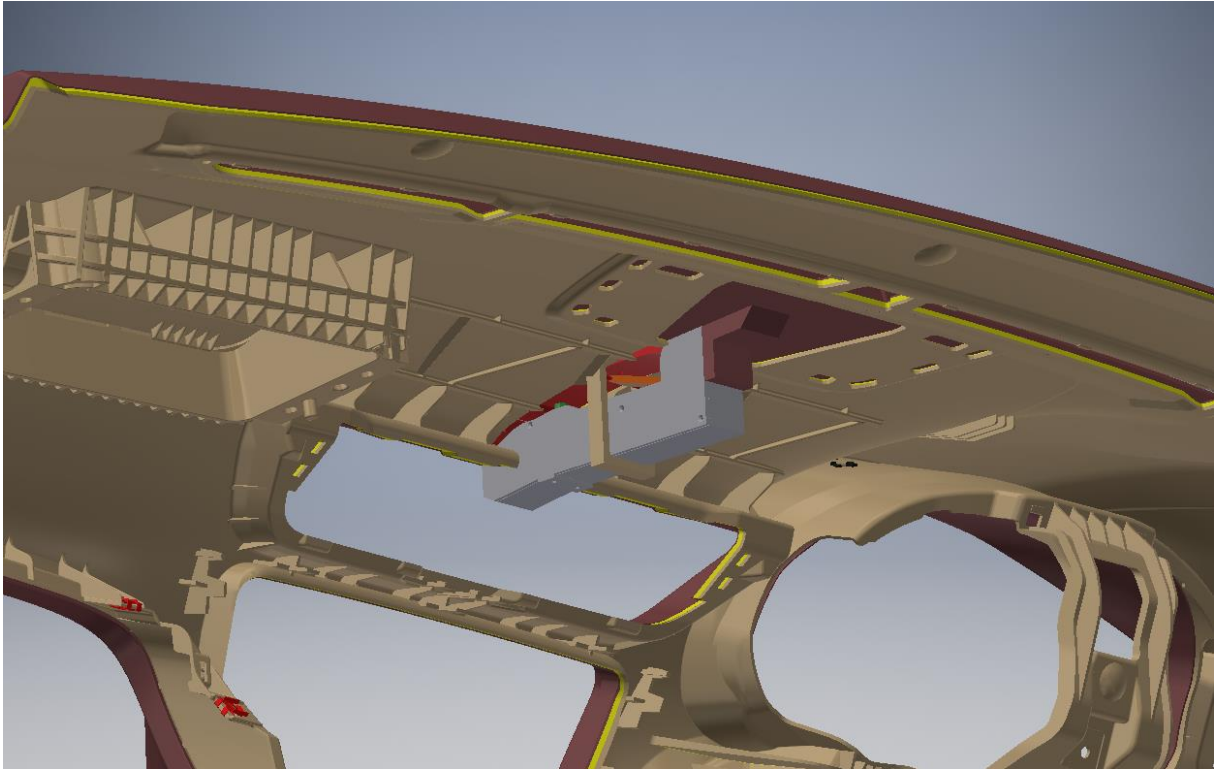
Zobrazení montážní díry pro šroubovák v U členu
